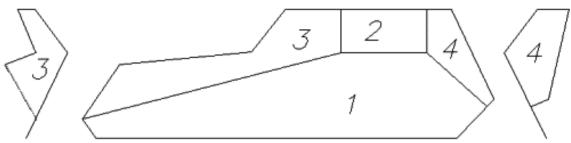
Начало развертки боковины корпуса бронеавтомобиля.
